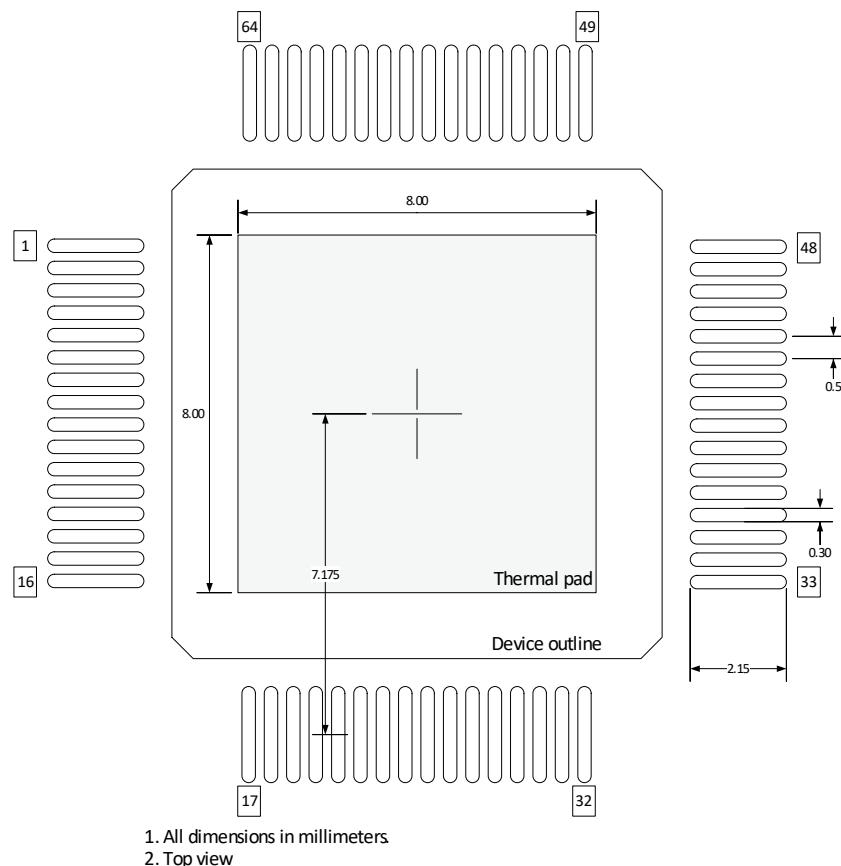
LMX2615-SP PCB 焊盘图案示例
